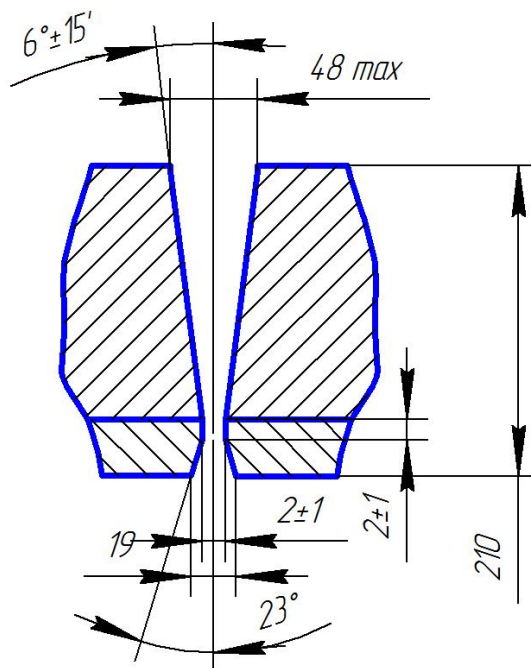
Форма разделки кромок под автоматическую сварку кольцевых швов рулонированных обечаек
